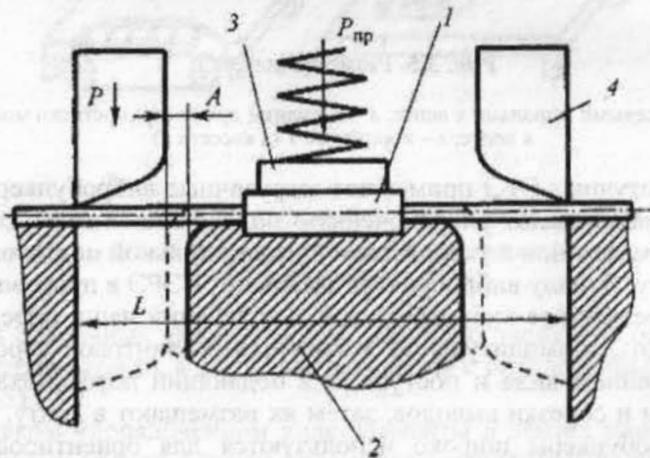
Схема обрезки и П-образной формовки осевых выводов в штампе:
